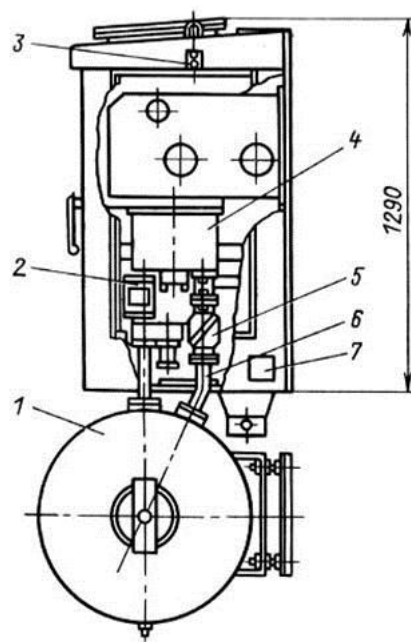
Пневматичний привод типу ШПВ-46П
